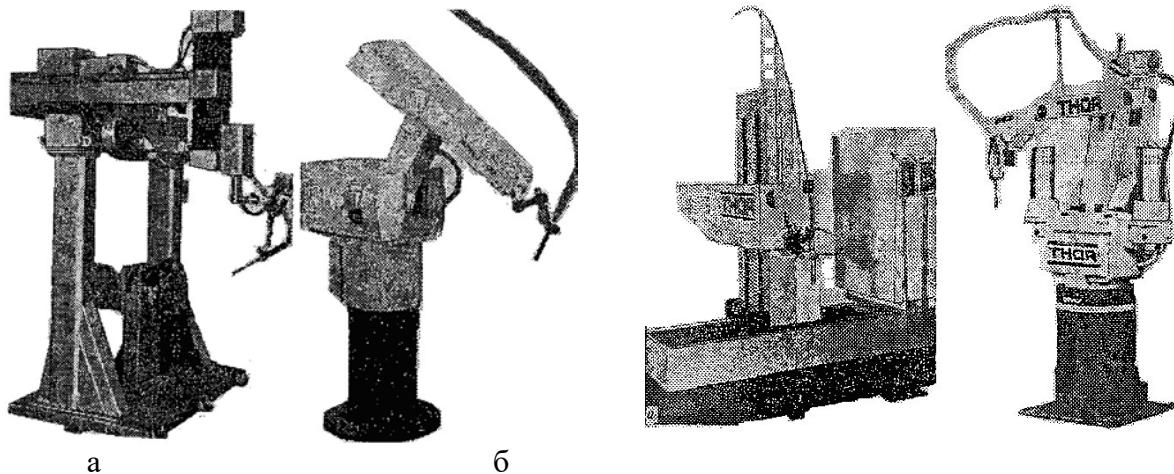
Роботи для зварювання фірми «Шин-Мейва» (Японія): а – PW752; б – RJ65
